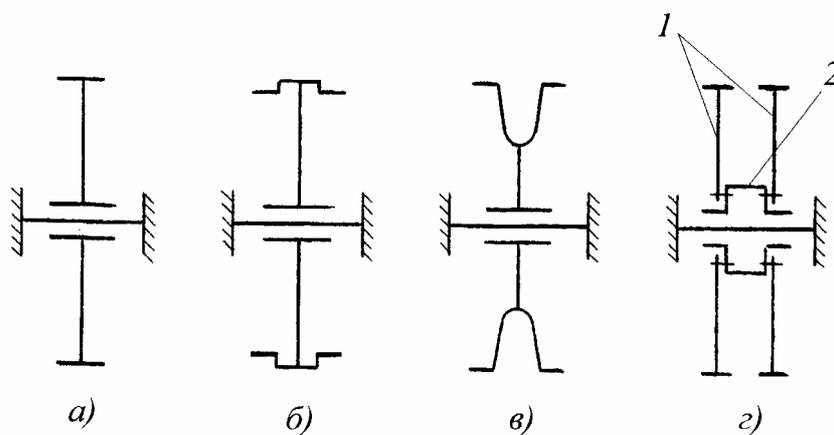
Схемы конструкций ободьев направляющих колес
